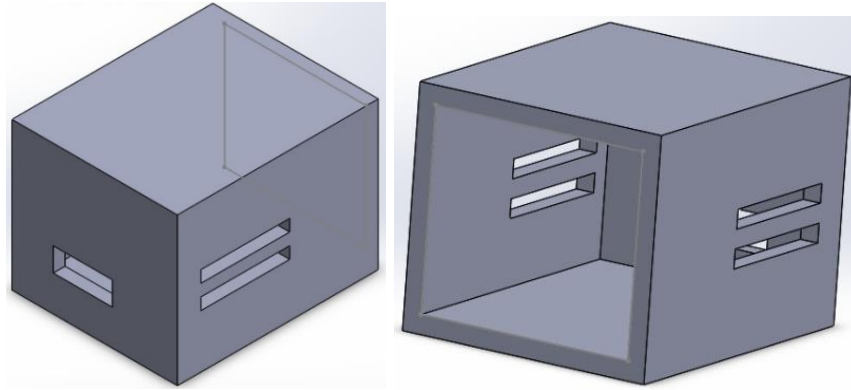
Diseño de la caja del bloque Driver de Actuadores
